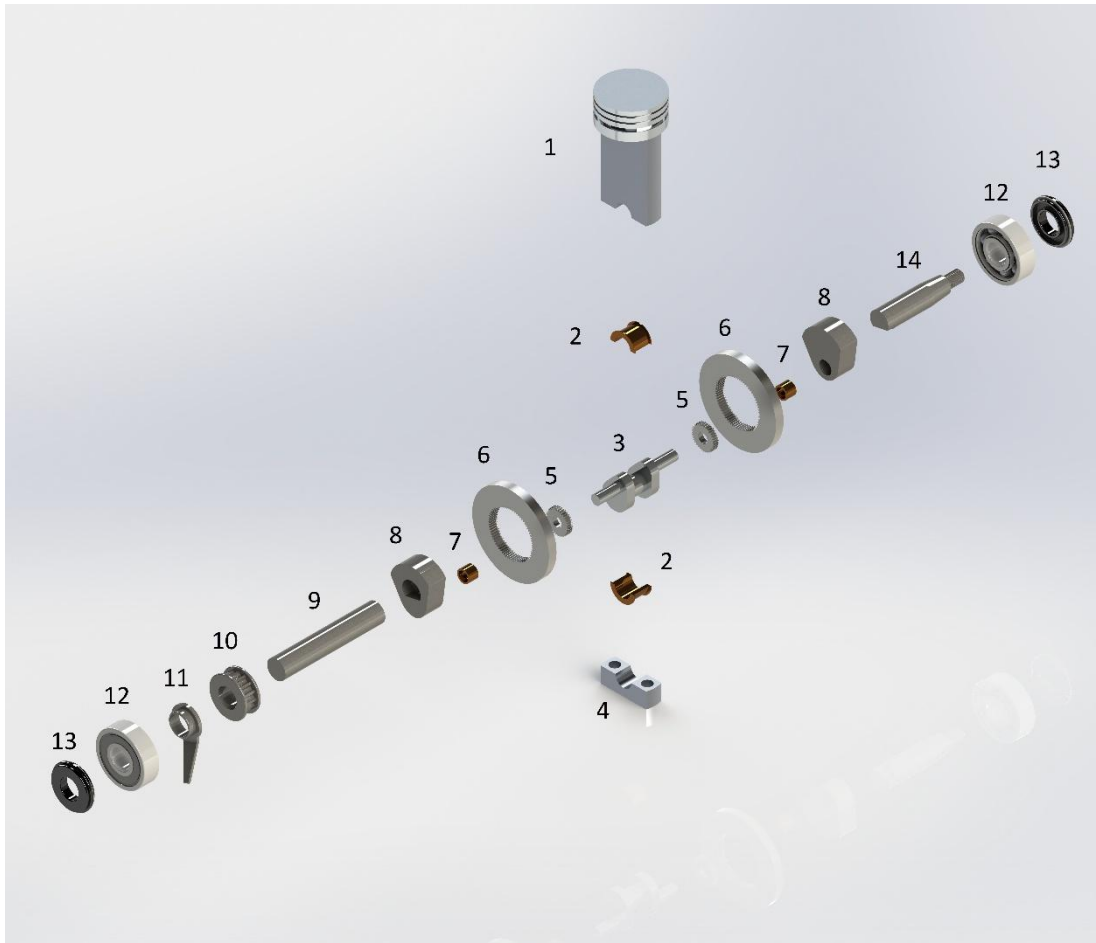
Vista explodida da montagem do protótipo do motor hipocicloide.
